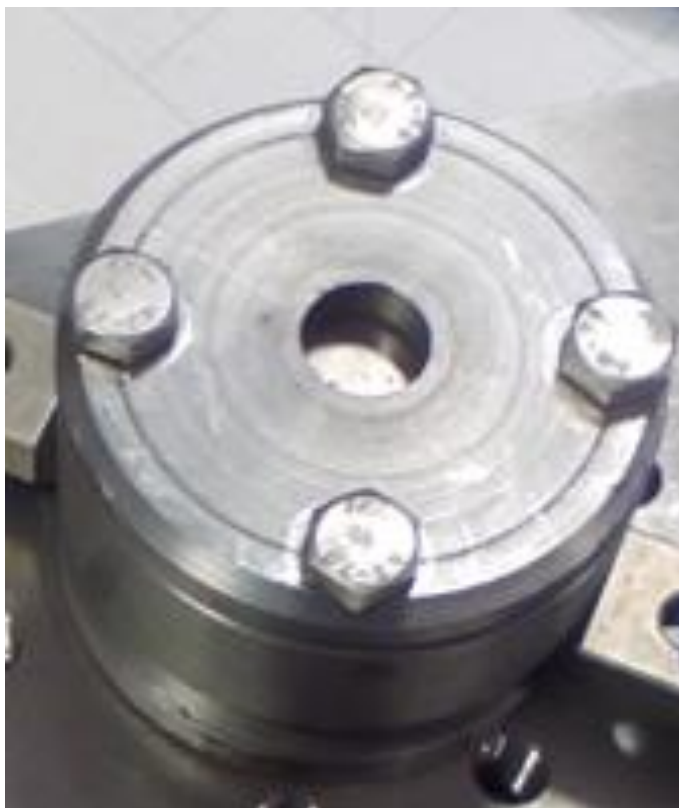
специальное приспособление, предотвращающее прогиб заготовки во время формообразования отверстия
